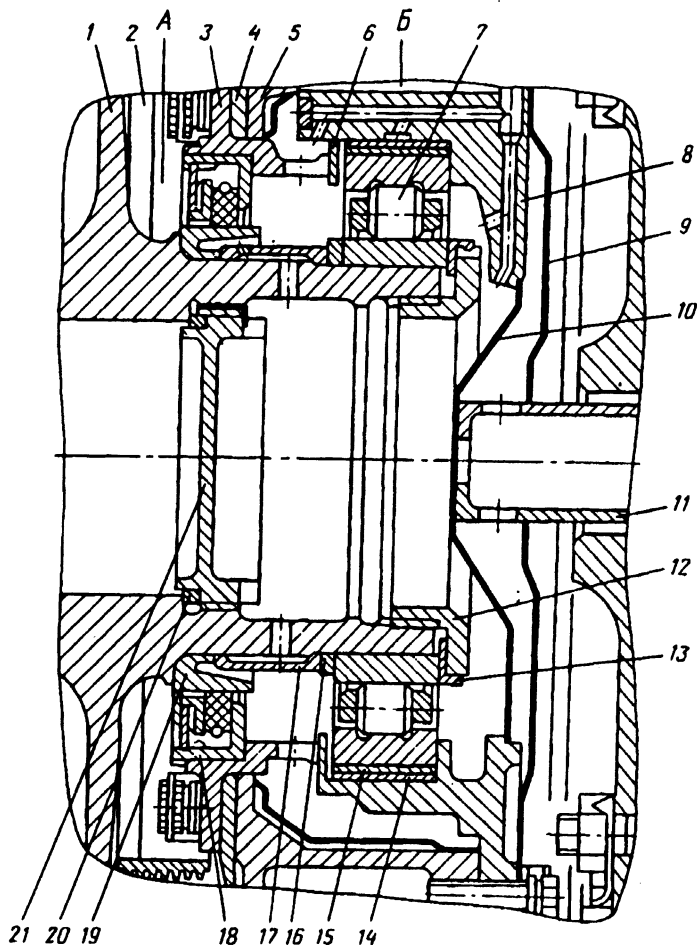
Опора турбины компрессора (третья опора двигателя):
